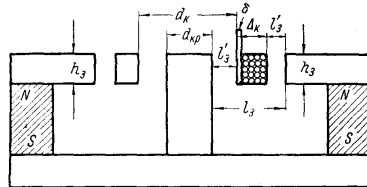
Основные конструктивные размеры рабочего зазора магнитной цепи.
